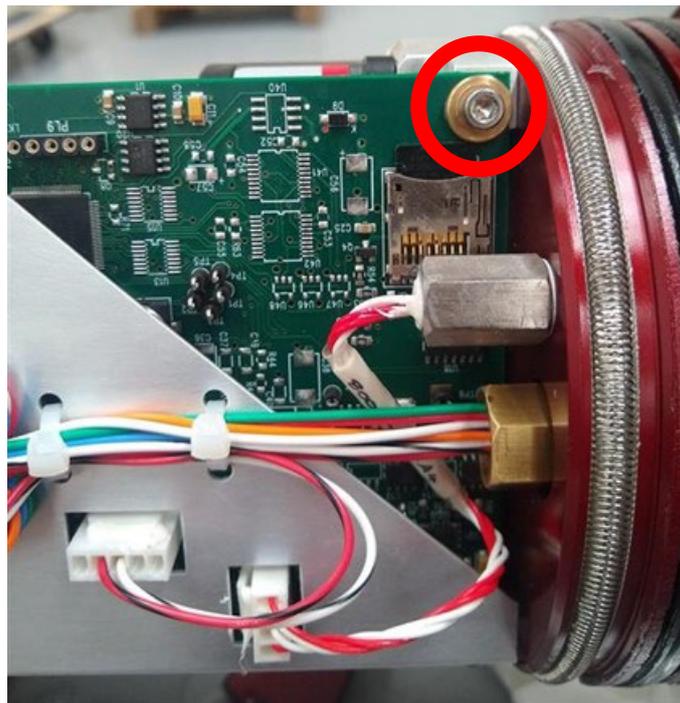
La placa DAS con MMC expuesta mientras la tapa del extremo del sensor se retira parcialmente
